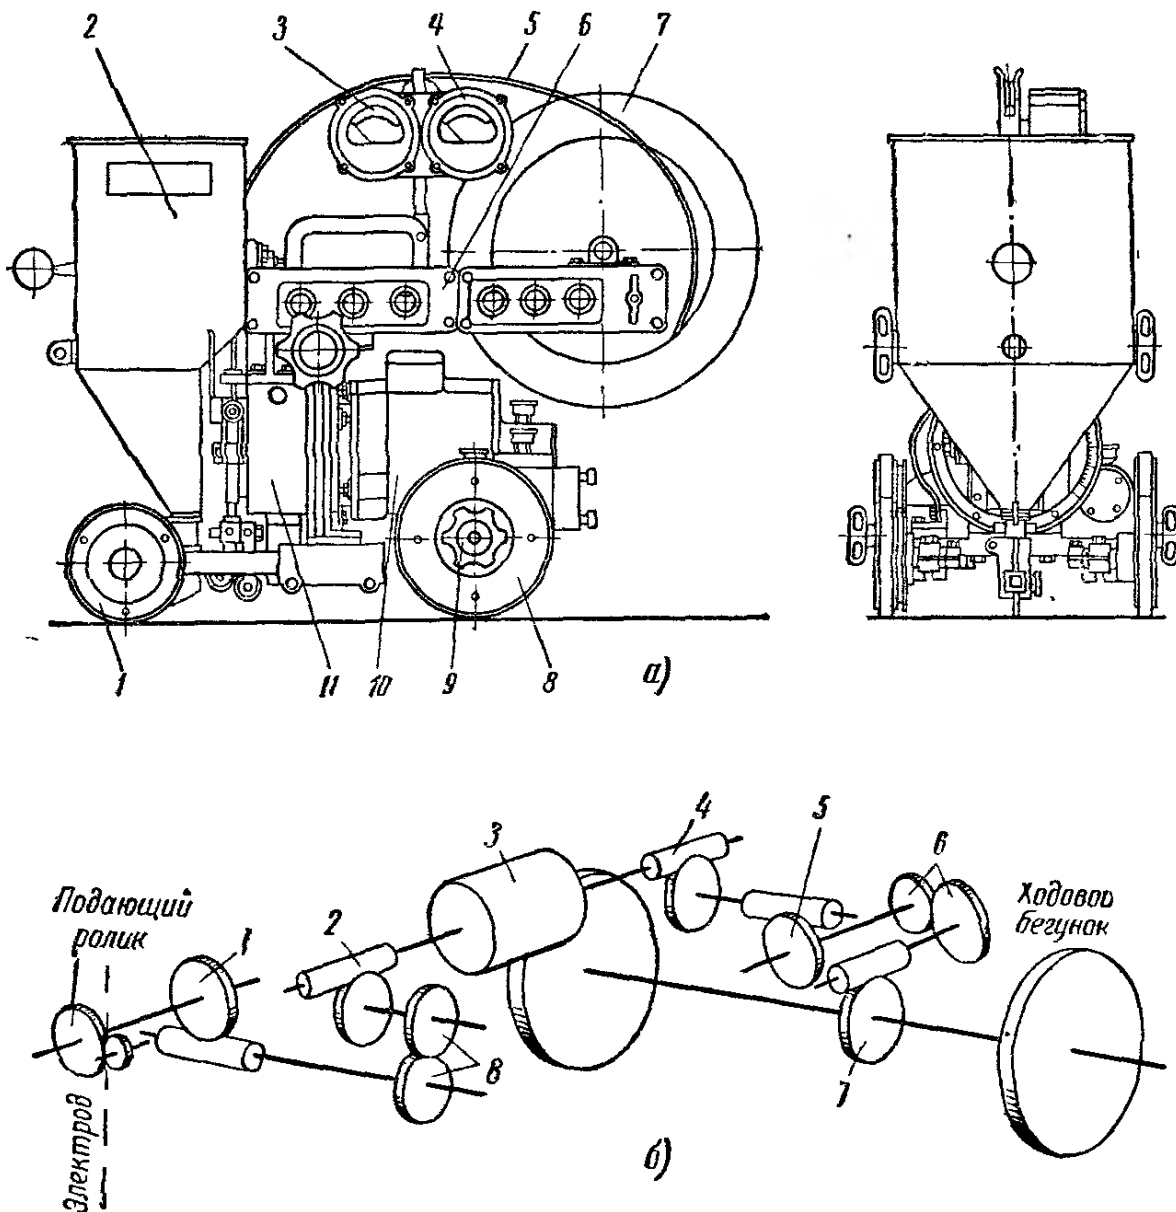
Сварочный трактор ТС-17-М-У:
